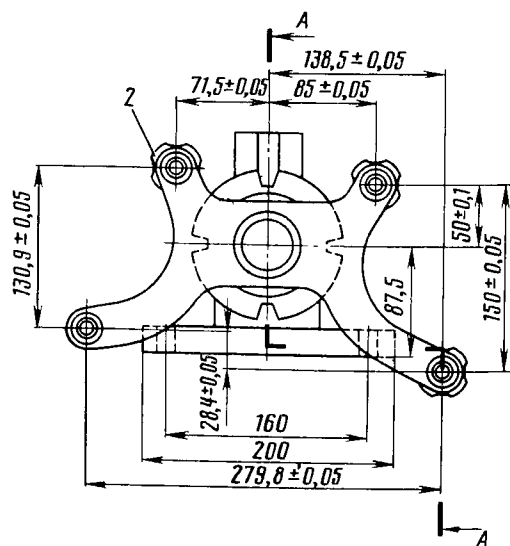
Приспособление для крепления двигателя при разборке и сборке:
